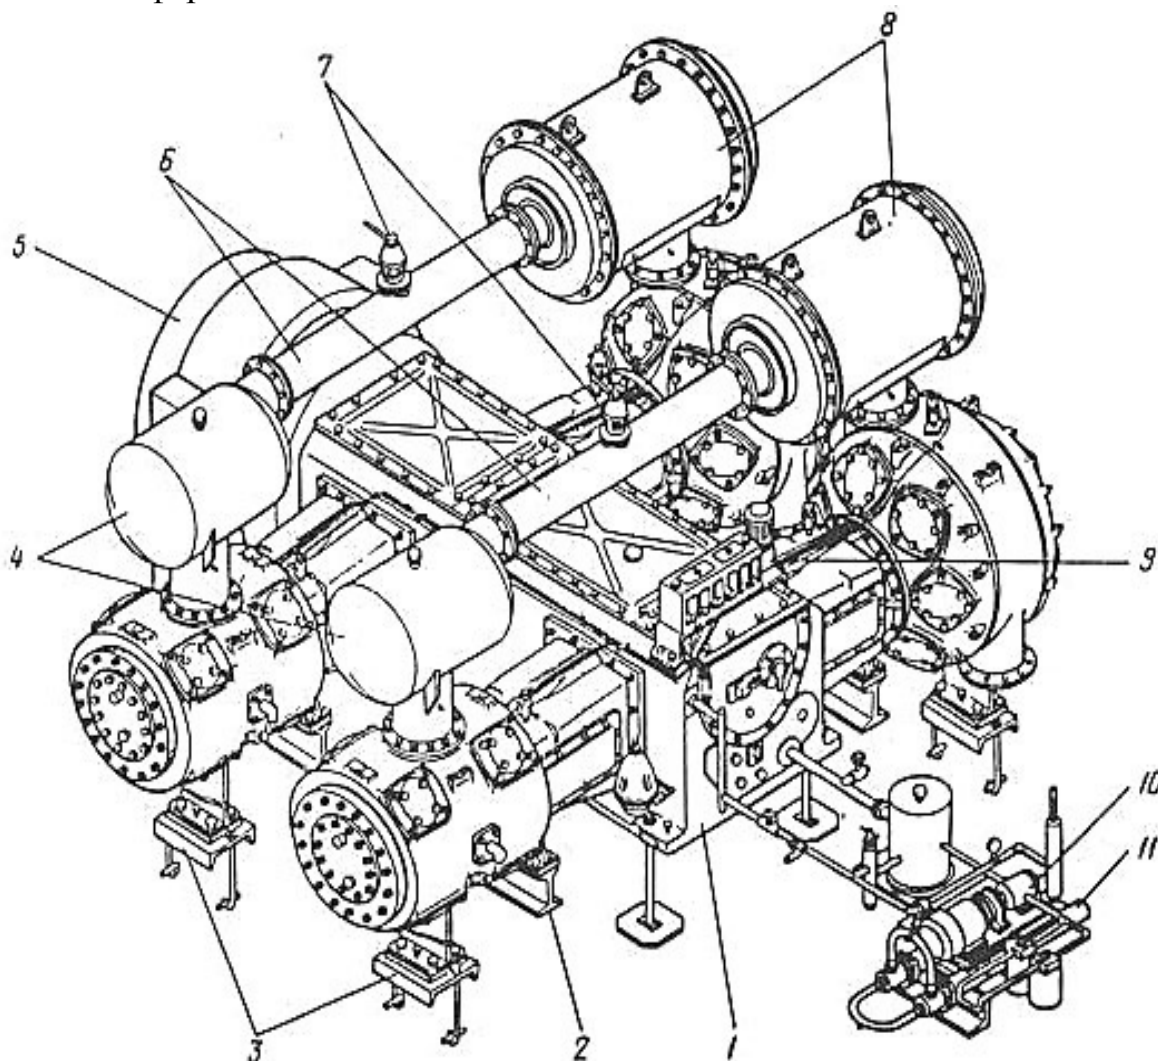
Устройство компрессора 4ВМ10-102/9
